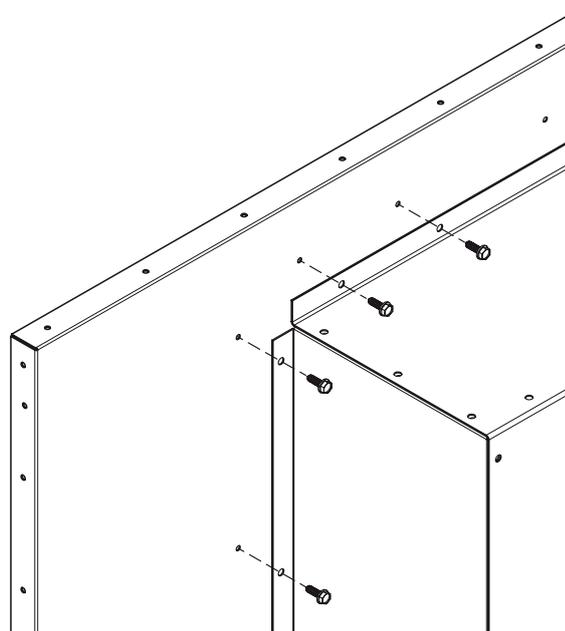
Dettagli di assemblaggio dei silenziatori laterali
